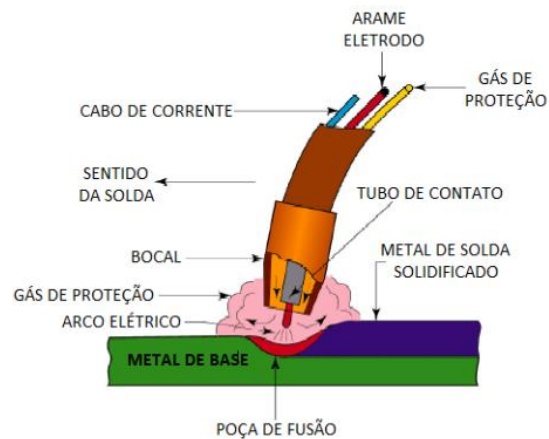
Diagrama esquemático do processo de soldadura semiautomática MIG-MAG [27]
